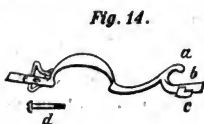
Der Handbügel, $\frac{1}{7}$ der wahren Größe; a der Schweiß; b der Fuß; c der Haken; d die Scheibenschraube; e das Loch für die Scheibenschraube.
